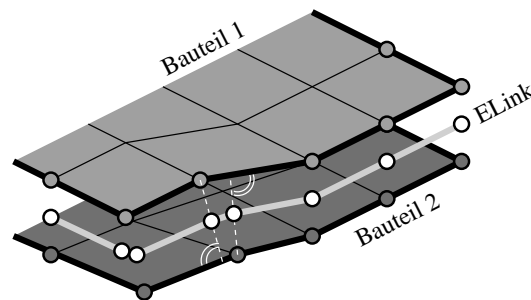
Die Stützpunkte einer Schweißnaht werden durch gegenseitige Projektion der Bauteilrandpunkte auf die benachbarte Bauteilkante und anschließende Mittelung gewonnen.
